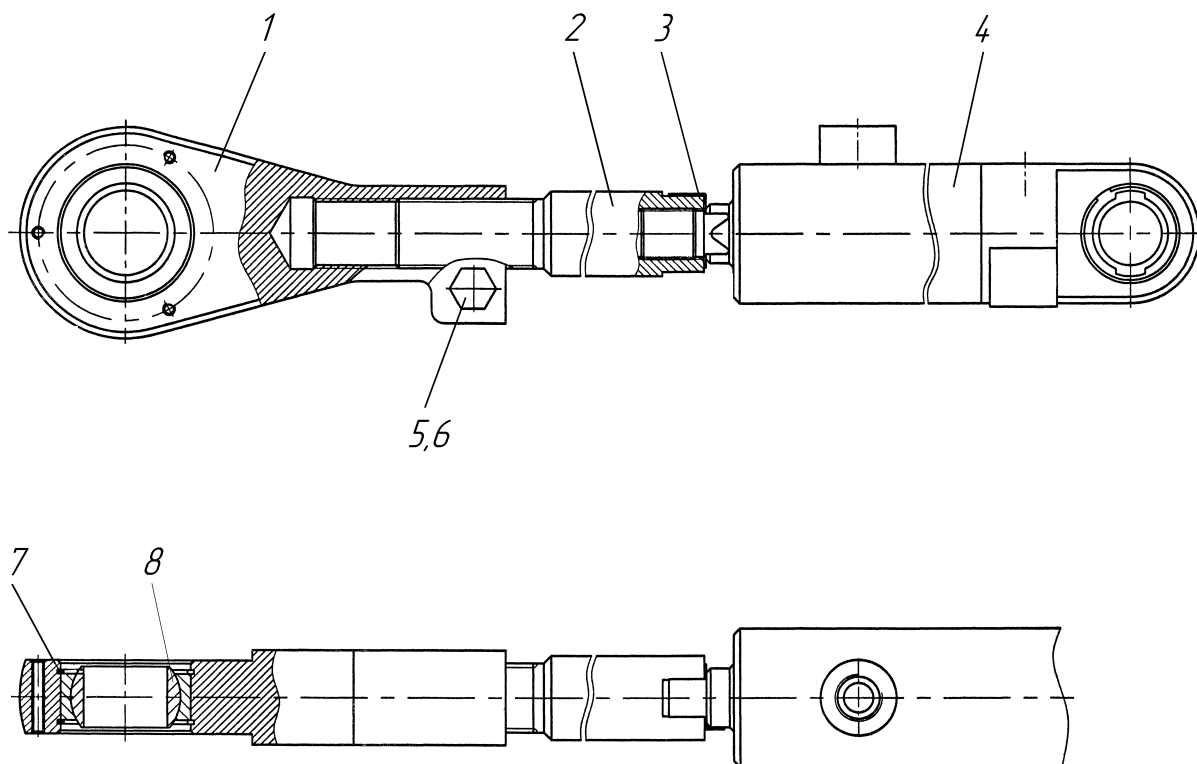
Цилиндр поворота 661.03.04.00.000
